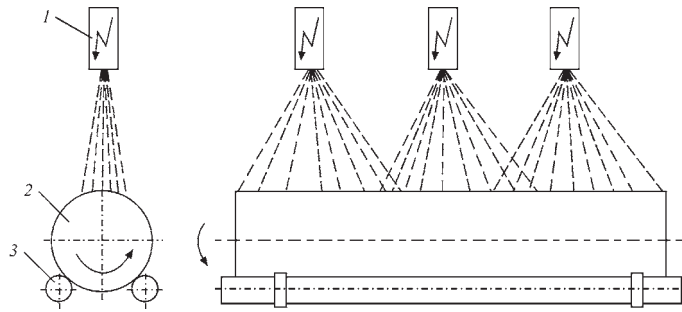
Схема оплавлення зливка: 1 — електронно-променева гармата; 2 — зливкок; 3 — валки
